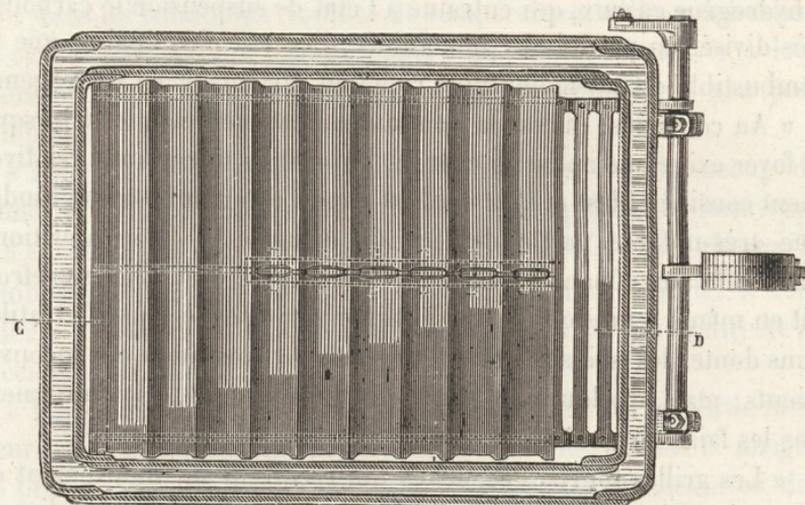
Plan d'un foyer à grille Chobrzynsky.
